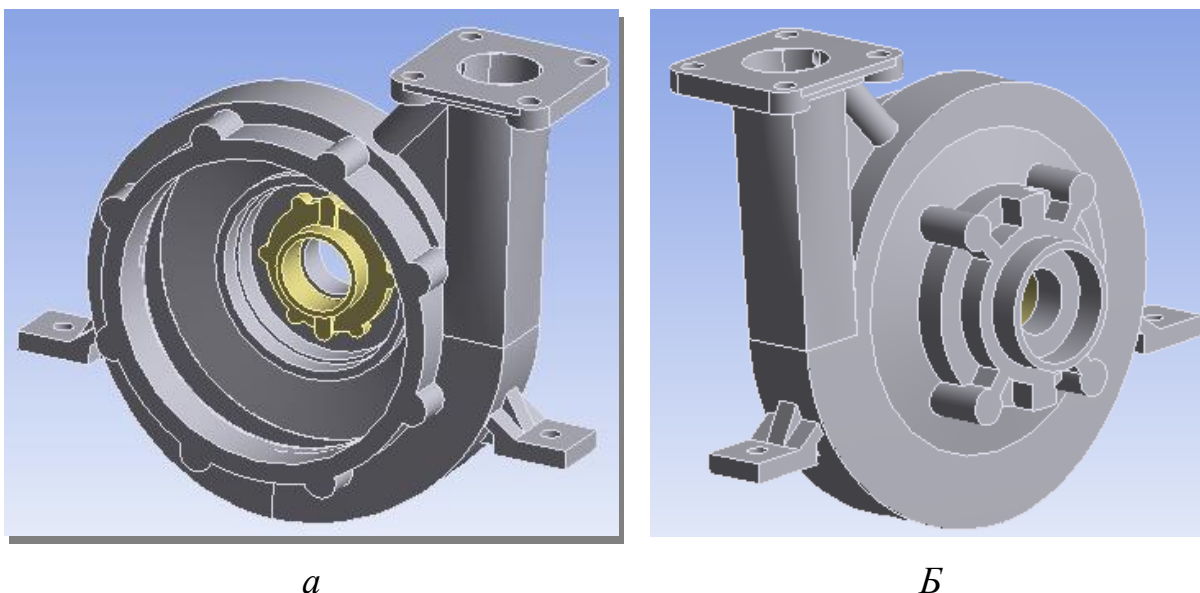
Просторова геометрія корпусу насоса ПН-40УВ
